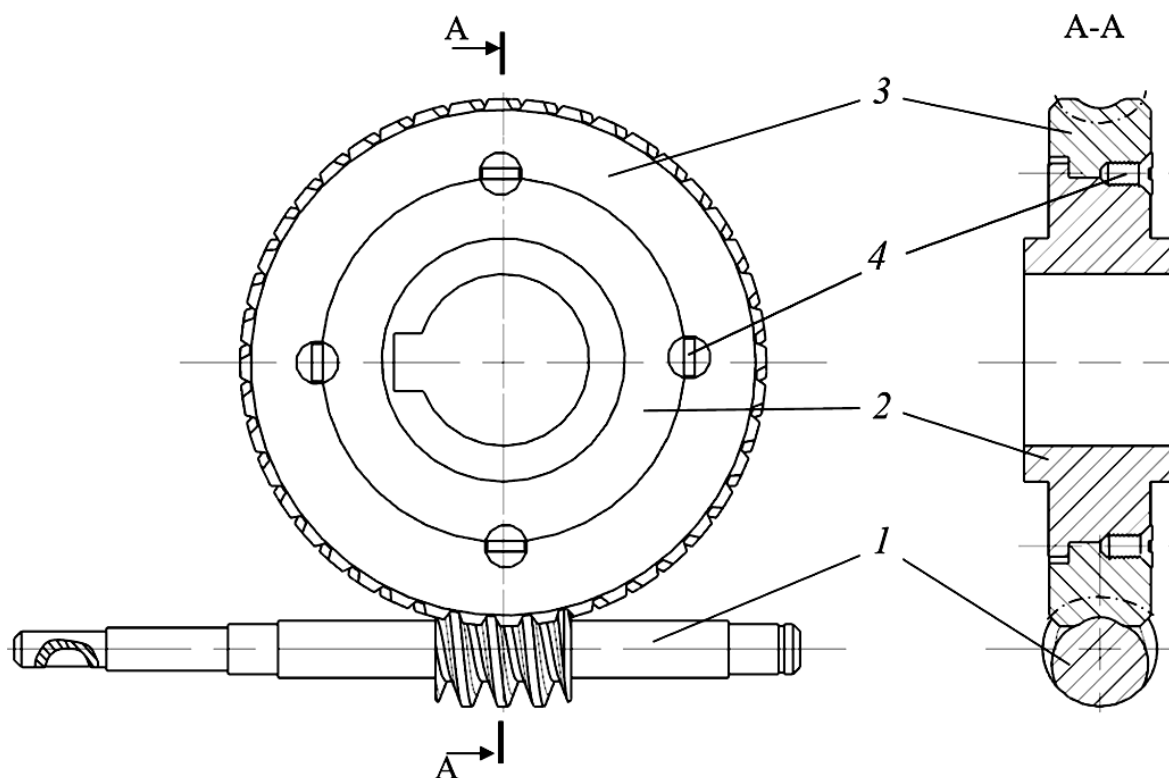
Основные детали червячной передачи: 1 – червяк; 2 – зубчатый венец червячного колеса; 3 – ступица червячного колеса; 4 – установочный винт
